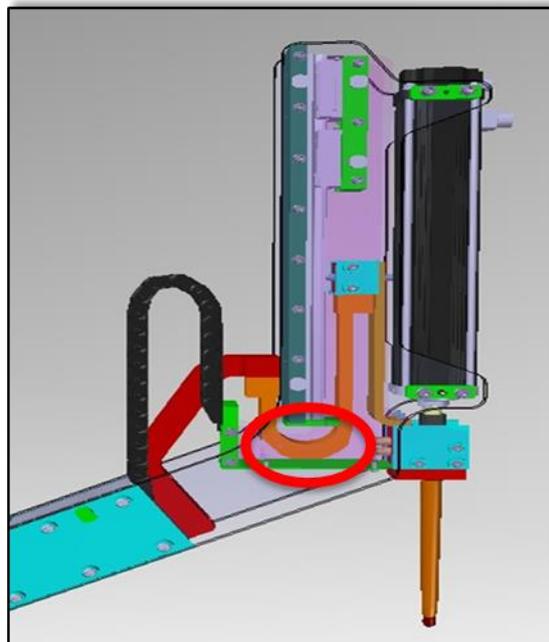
Conduttore che urtava durante la movimentazione del Robot sul carter inferiore.
